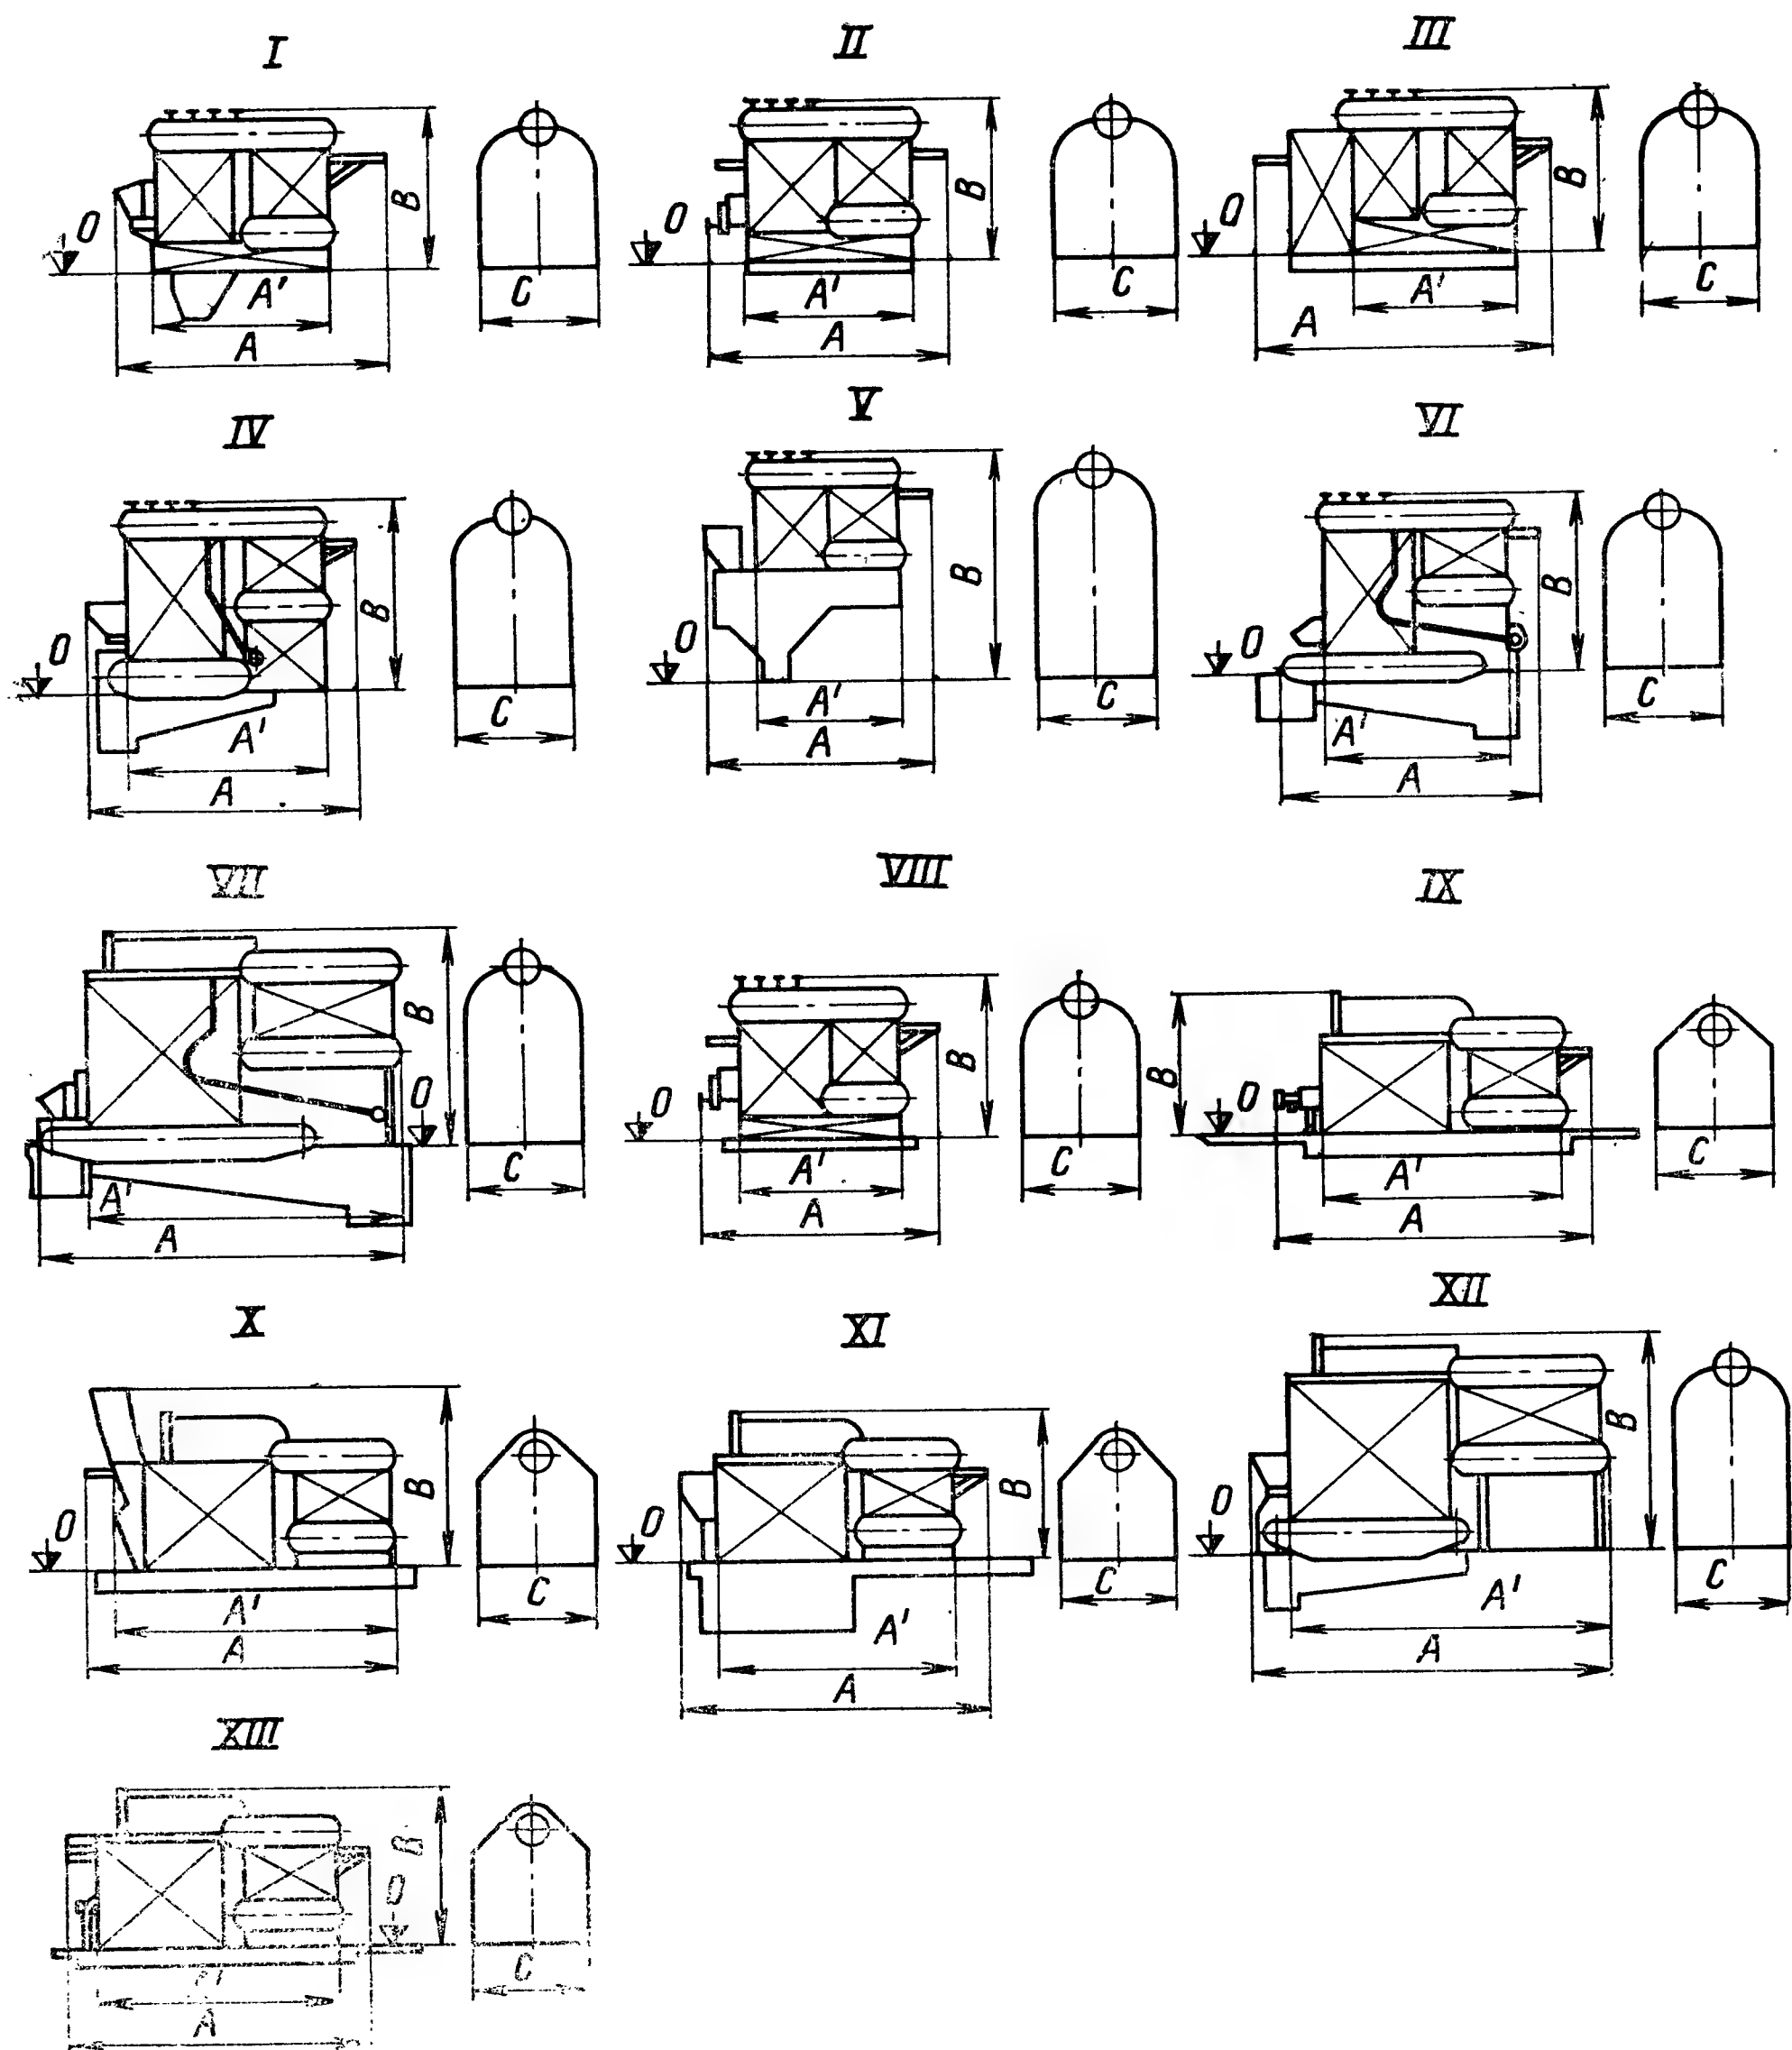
Схемы компоновок котлов типа ДКВР с различными топочными устройствами и габаритные размеры (в объеме заводской поставки).
